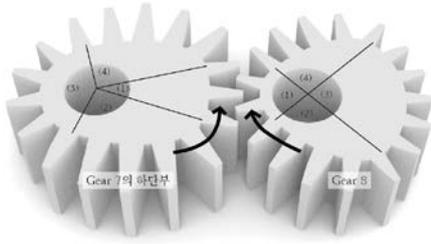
특수 변속 메커니즘 위한 기어 (Gear 7,8)
